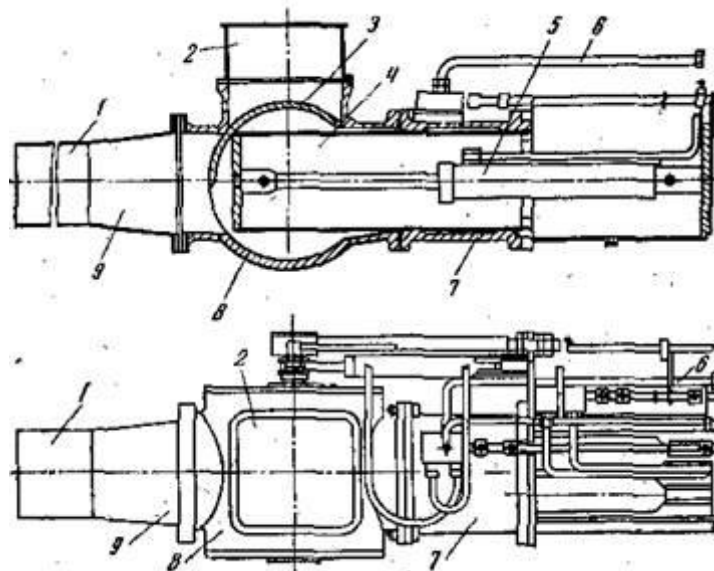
Вид зверху і вид з боку установки УТН-10:
